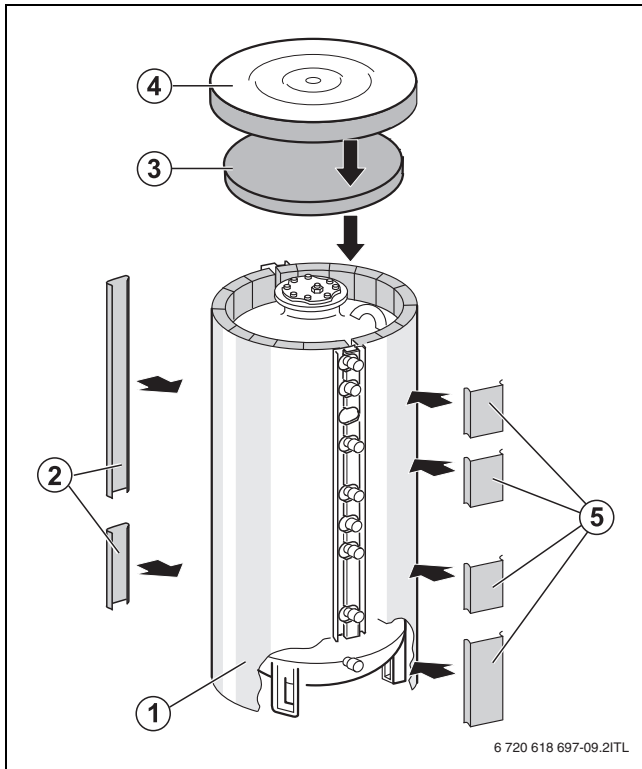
Abdeckleisten und obere Wärmedämmung montieren (Ansicht von hinten)
